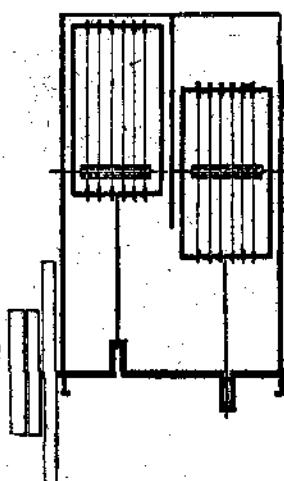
Схема лесопильного станка с двумя рамами, движущимися в противоположные стороны.
